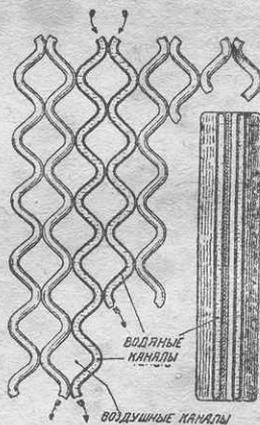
а. Пластиначный радиатор с зигзагообразными лентами.
